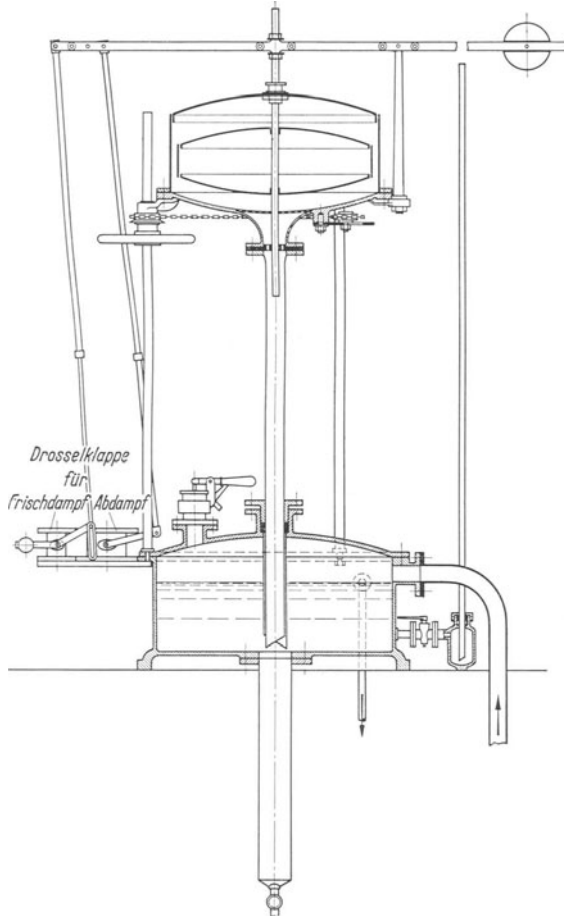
Selbsttätig arbeitender Dampfdruckregler (Maschinenbau-Akt.-Ges. Golzern-Grimma, Grimma, Sa.).
